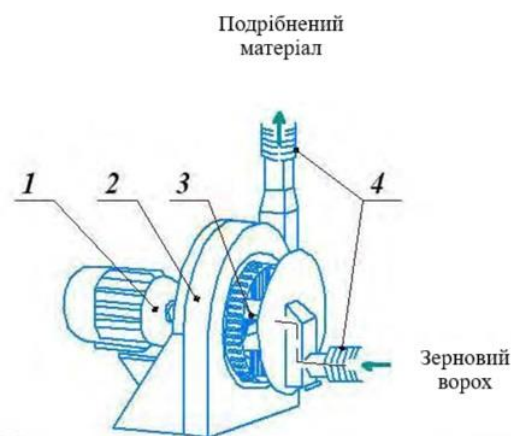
Схема переміщення зернового вороху під час роботи дробарки зерна серії ДКР: 1 – електродвигун; 2 – корпус дробарки; 3 – молотковий барабан; 4 – транспортувальні рукави.
